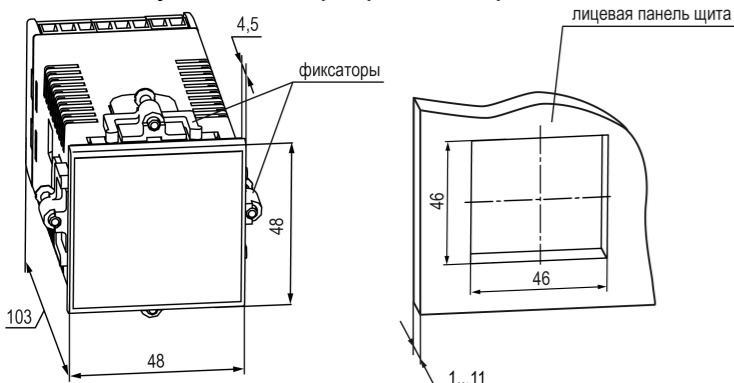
Габаритные размеры корпуса Щ5 и монтажного отверстия в щите
